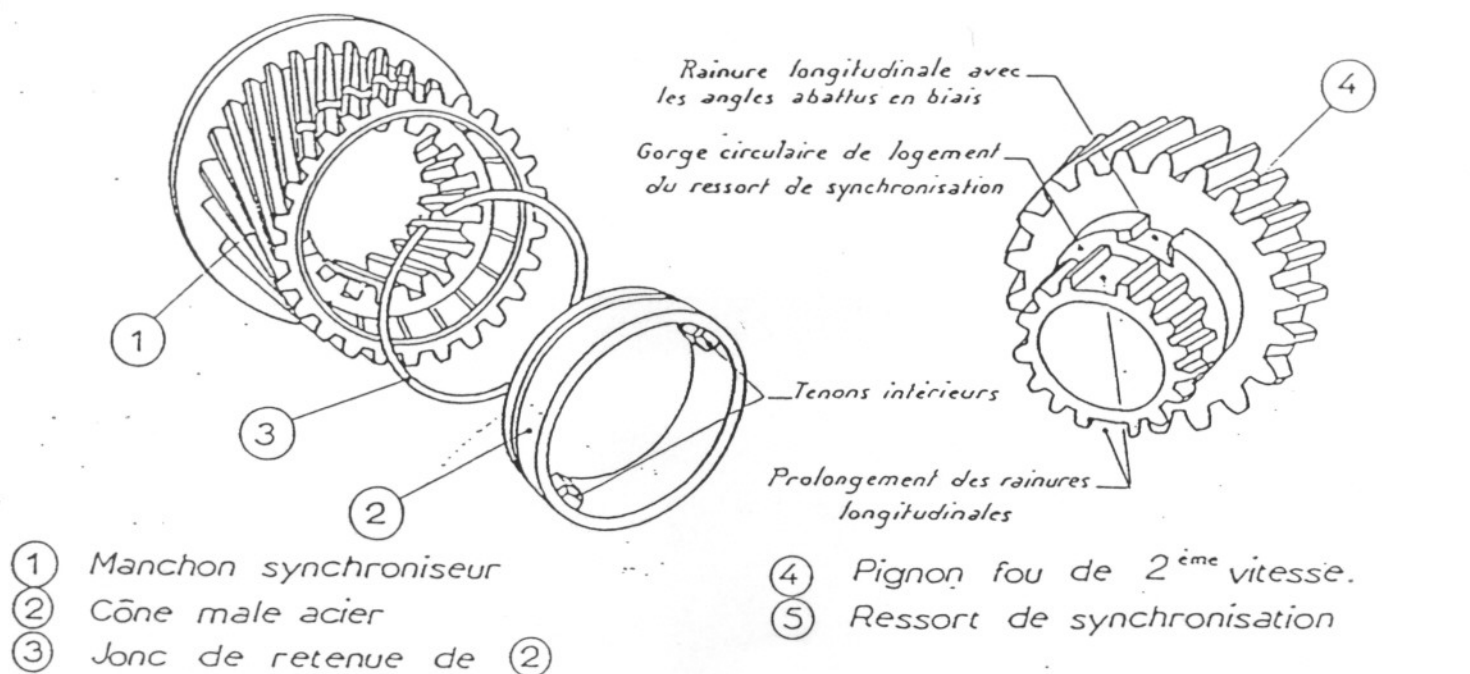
Vue éclatée de l'ensemble du synchroniseur
